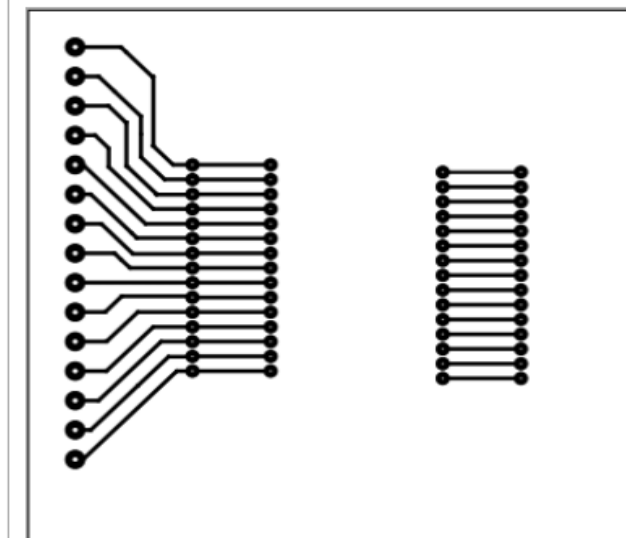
Diseño PCB del circuito para el control de la cortina
